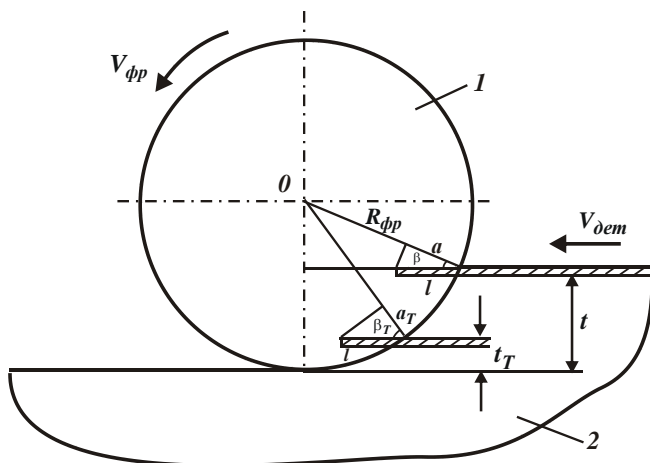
Расчетная схема параметров фрезерования цилиндрической фрезой:
